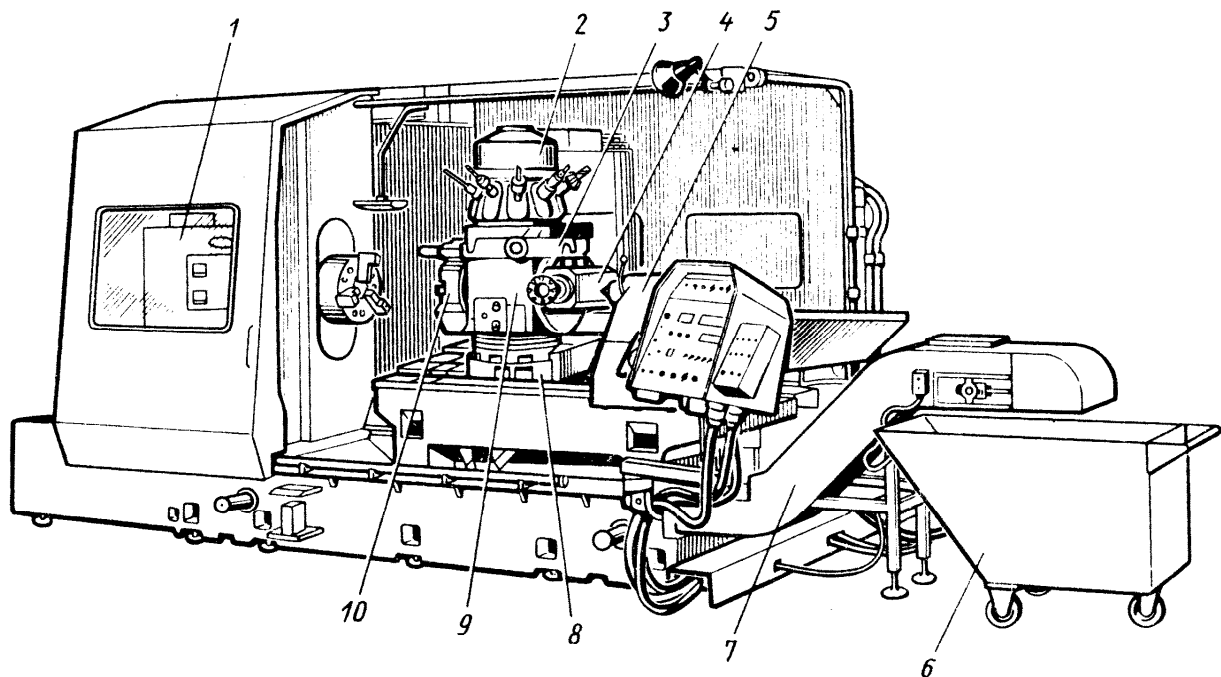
Токарний багатоопераційний верстат LM70-AT
